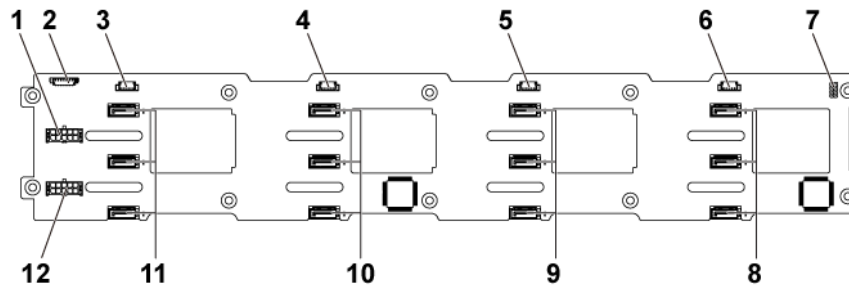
Vue arrière du fond de panier de disque dur de 3,5 pouces
